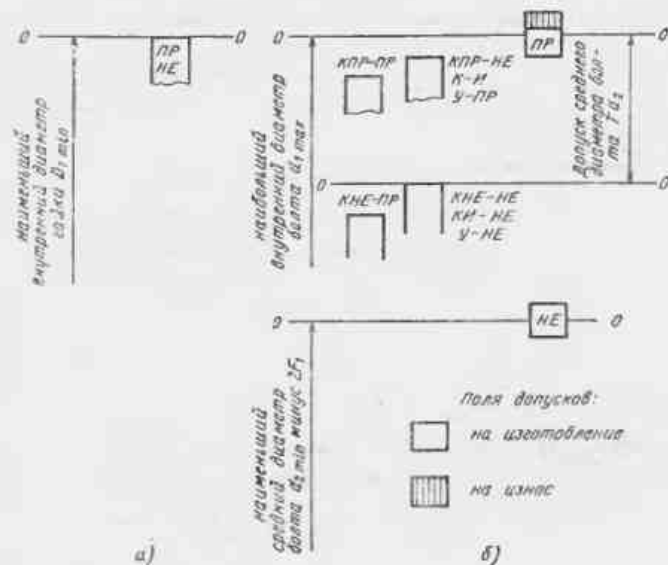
Схема расположения полей допусков внутреннего диаметра резьбы калибров для проверки: а — гайки; б — болтов
